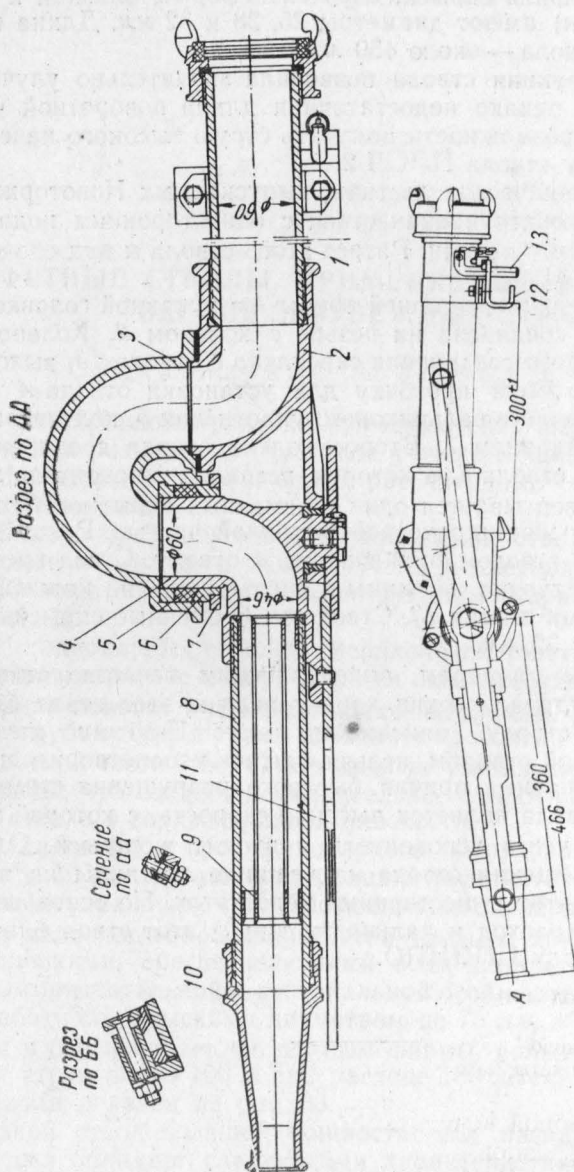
Ствол для автомеханических лестниц конструкции Новоторжского завода противопожарного оборудования:
